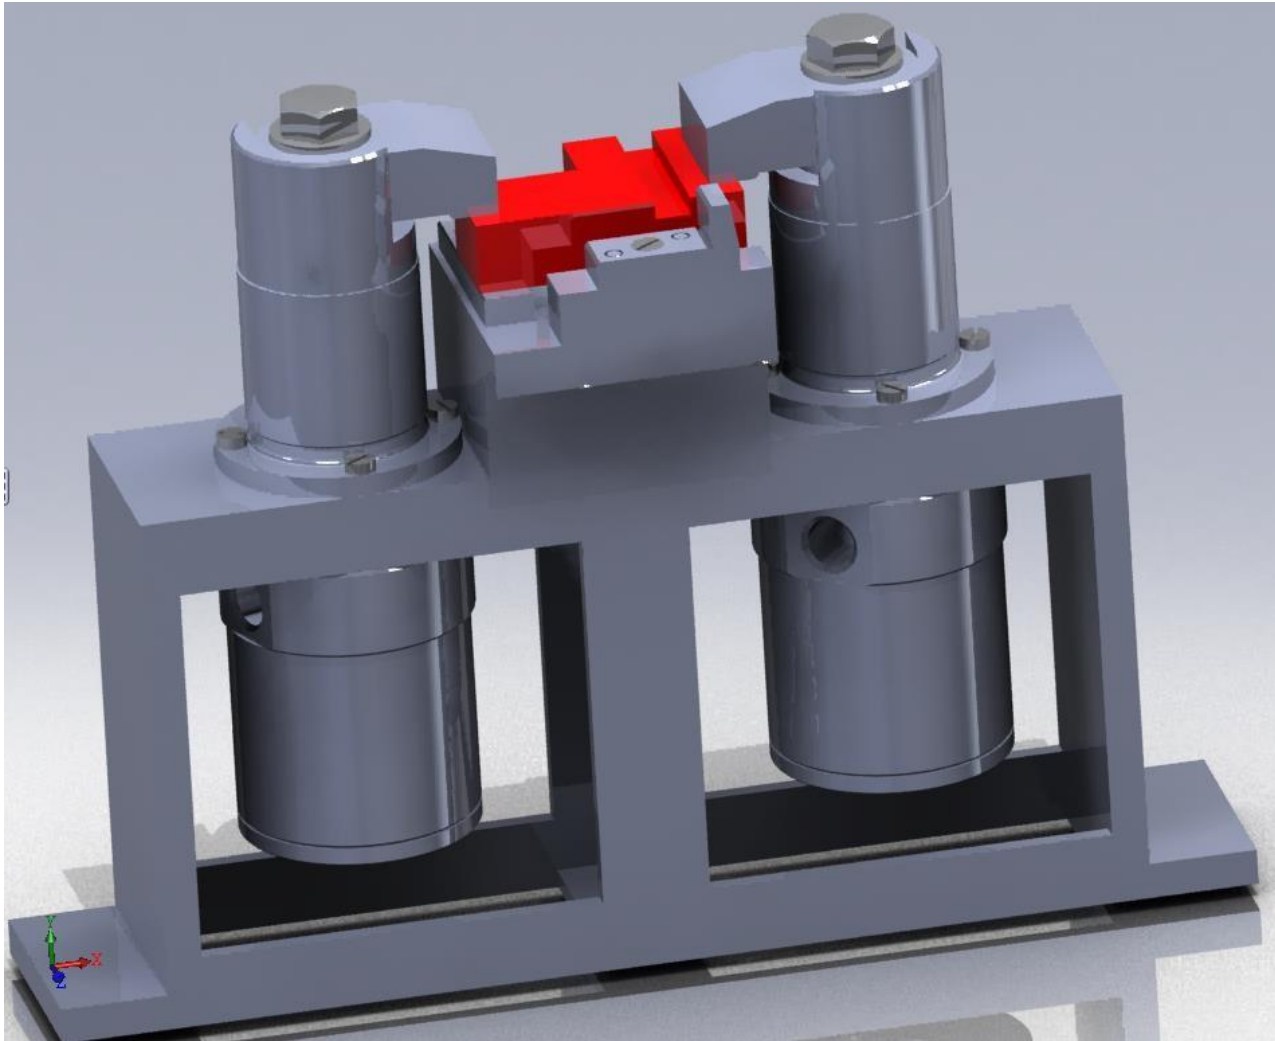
Базовый набор деталей и сборочных единиц универсально-сборных приспособлений:
